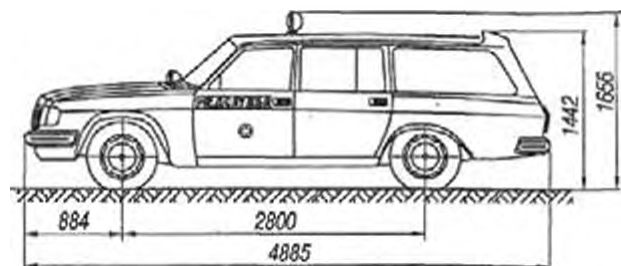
Автомобиль "Волга" ГАЗ-31023 и его габаритные размеры
